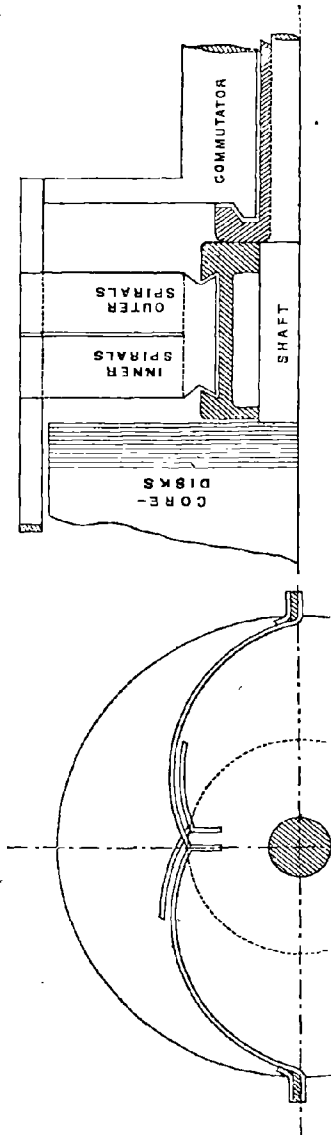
(Crompton) Bobinage en tambour de machine bipolaire pour stations centrales.
